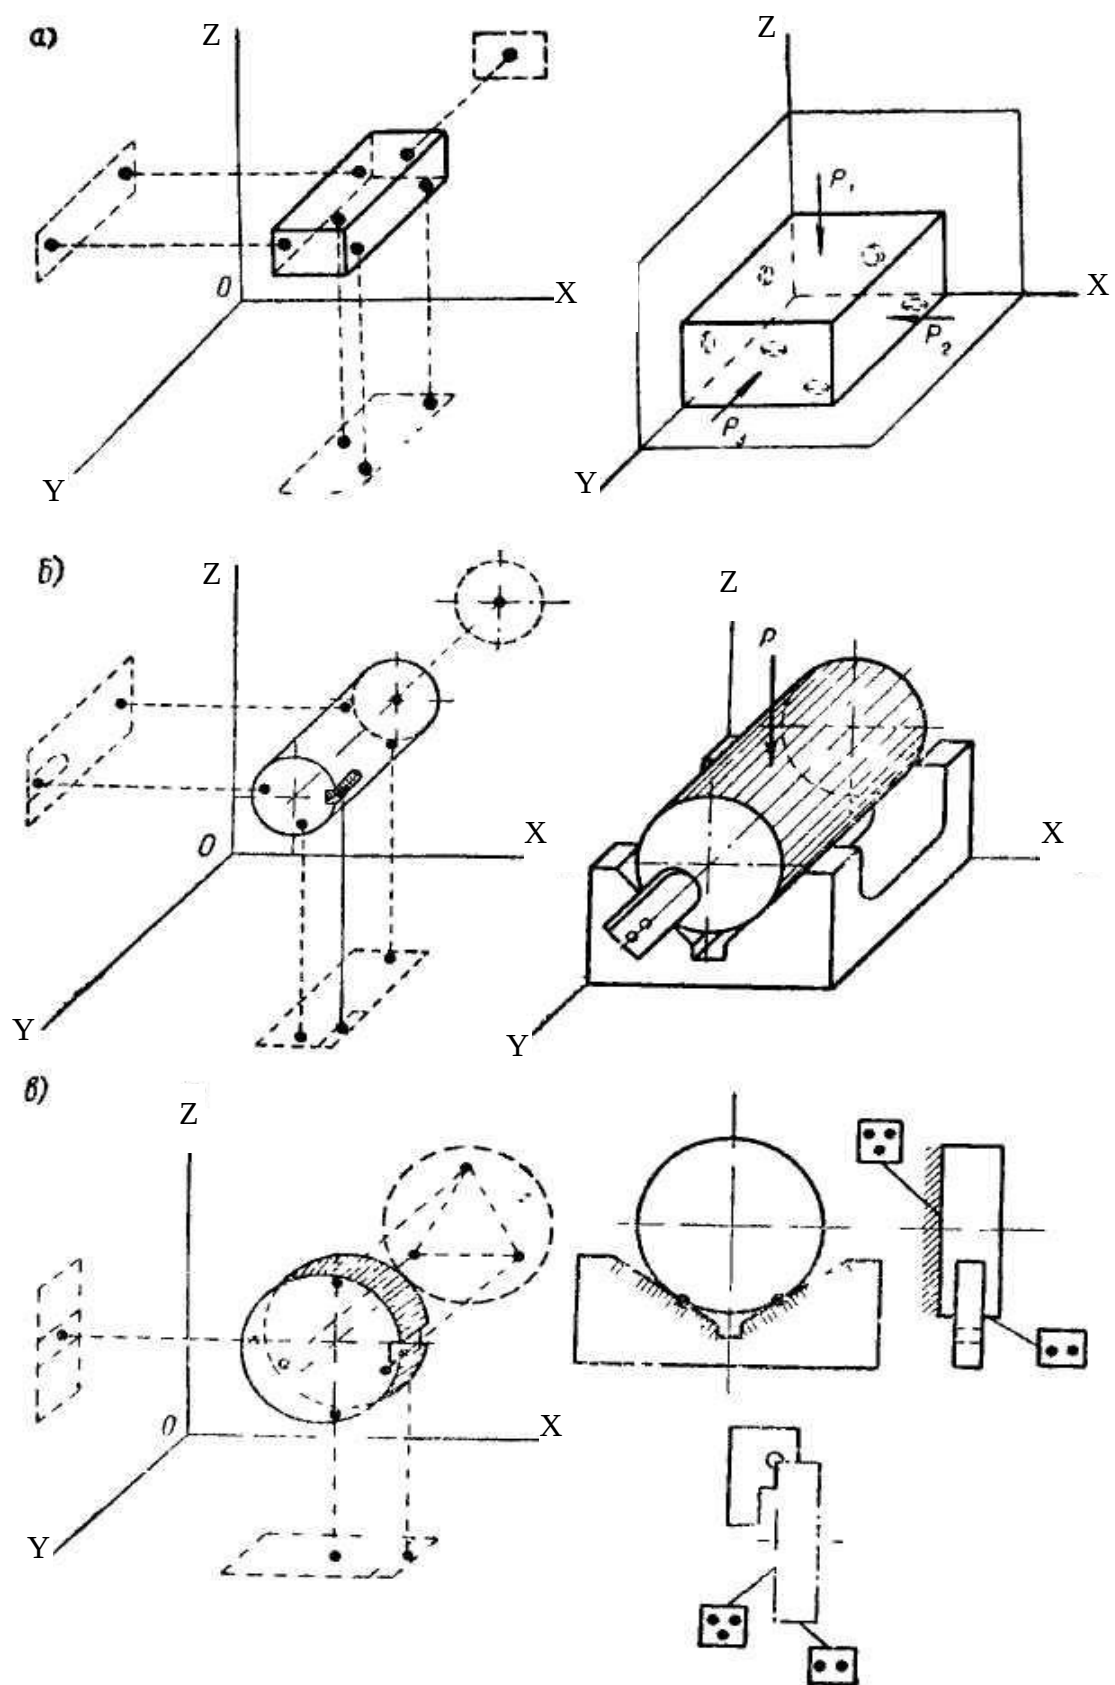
Схеми базування поверхонь у пристосуваннях
